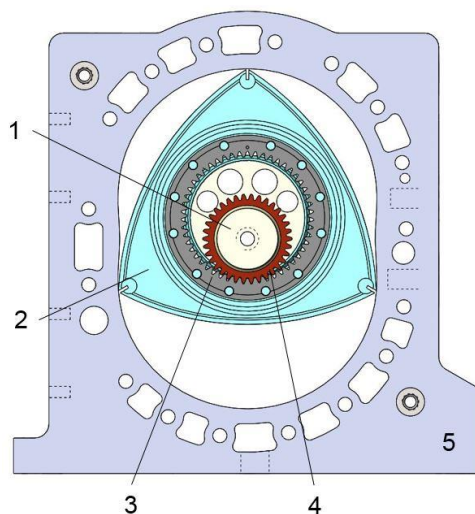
Схема РПД. 1-Эксцентриковый вал; 2-Ротор; 3-Шестерня ротора; 4-Неподвижная (малая) шестерня; 5-Статор.
